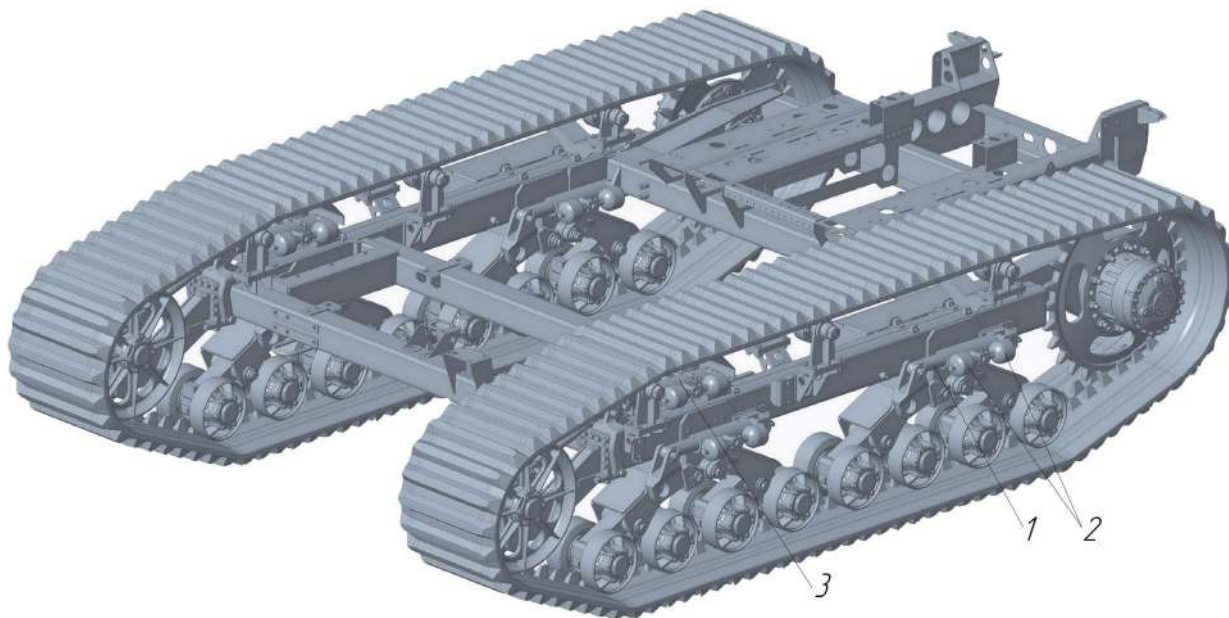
Общий вид гусеничной тележки самоходной рисоуборочной косилки с гидропневматической подвеской: 1 – гидроцилиндр подвески; 2 – пневмоаккумулятор; 3 – гидроцилиндр механизма натяжения
